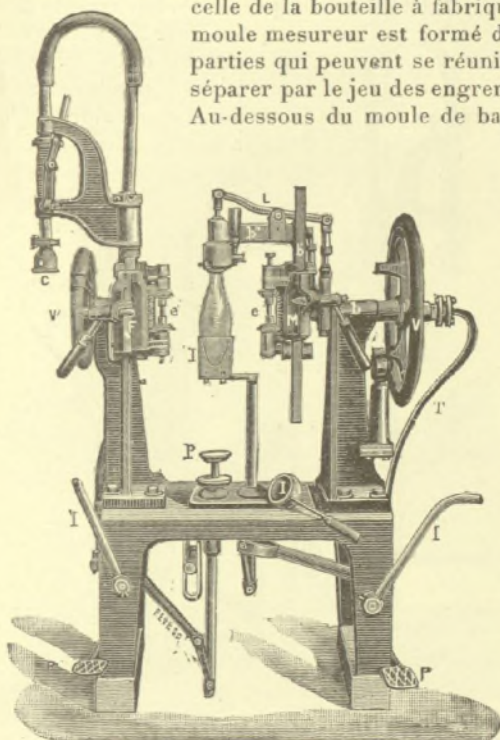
Machine C. Boacher pour la fabrication mécanique des bouteilles.
